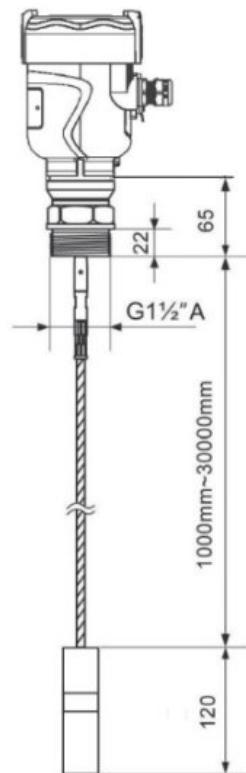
Габаритные размеры корпуса преобразователя сигналов уровнемера
